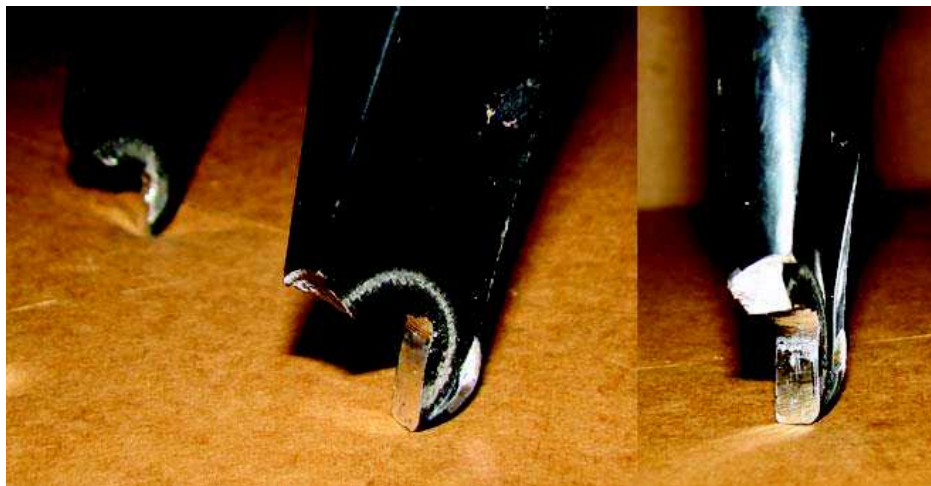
Ejemplo de rotura de la horquilla de aluminio por la fuerza de torsión
